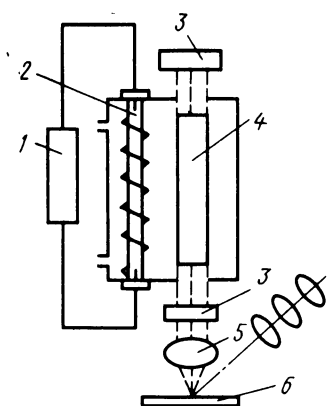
Сварочный оптический квантовый генератор:
